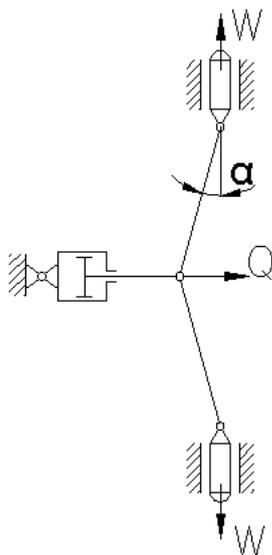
Конструктивная схема рычажно-шарнирного механизма
